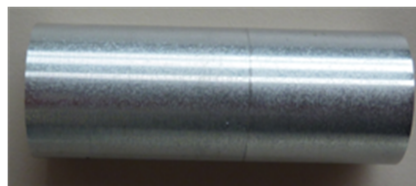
Probeta de partida para la forja del engranaje.
